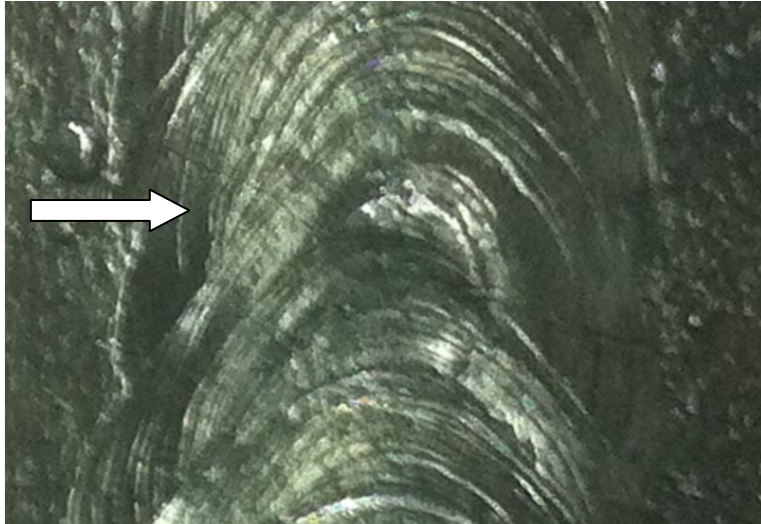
Fisura transversal al cordón de soldadura
